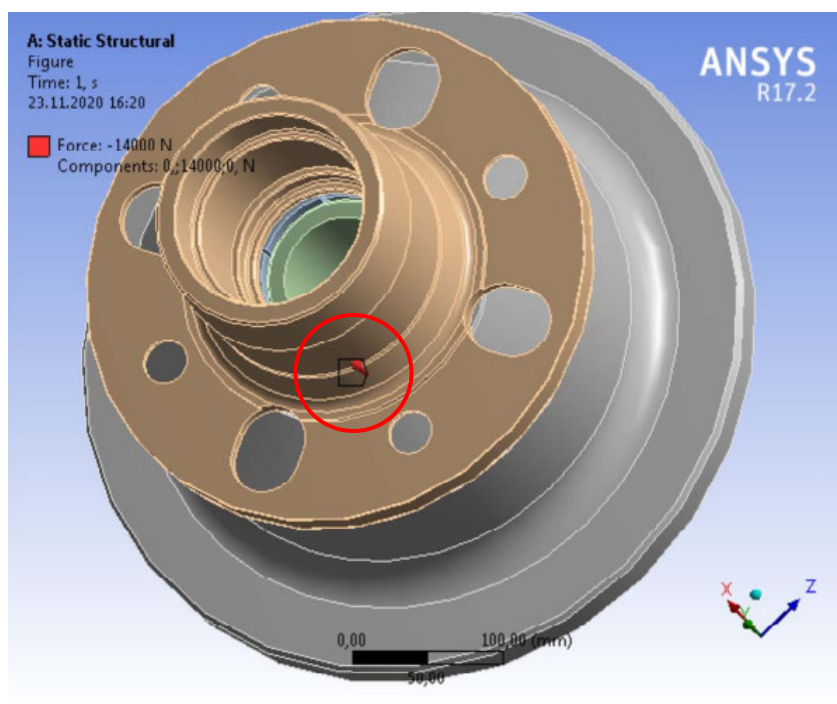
Дія зусилля з боку приводу затискання заготовки
